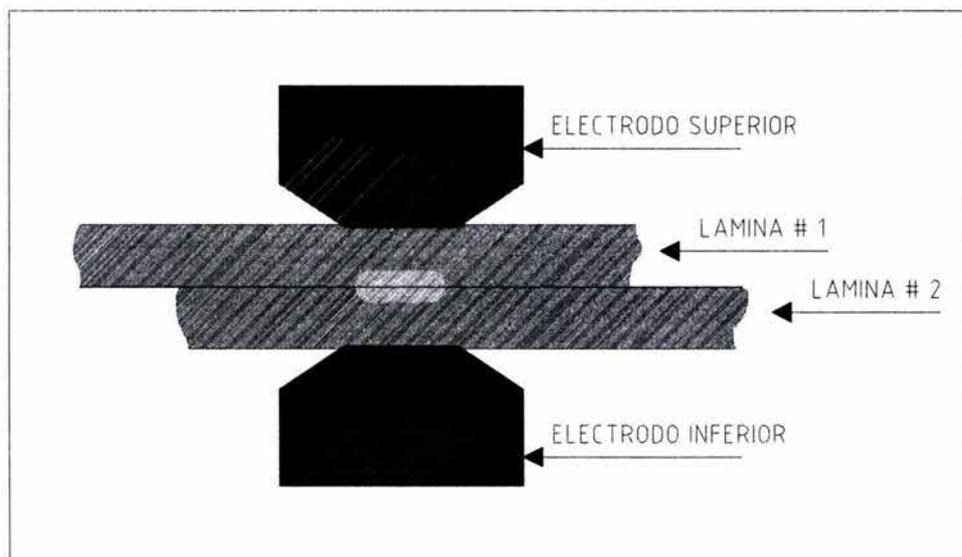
Materiales finales involucrados en el proceso de soldadura por resistencia.
